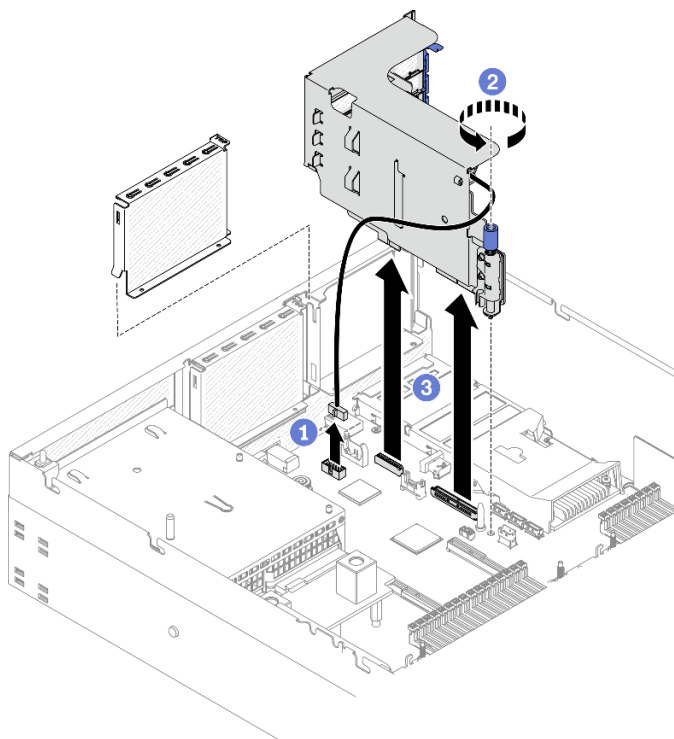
Removendo a placa riser PCIe 1 instalada com porta serial
